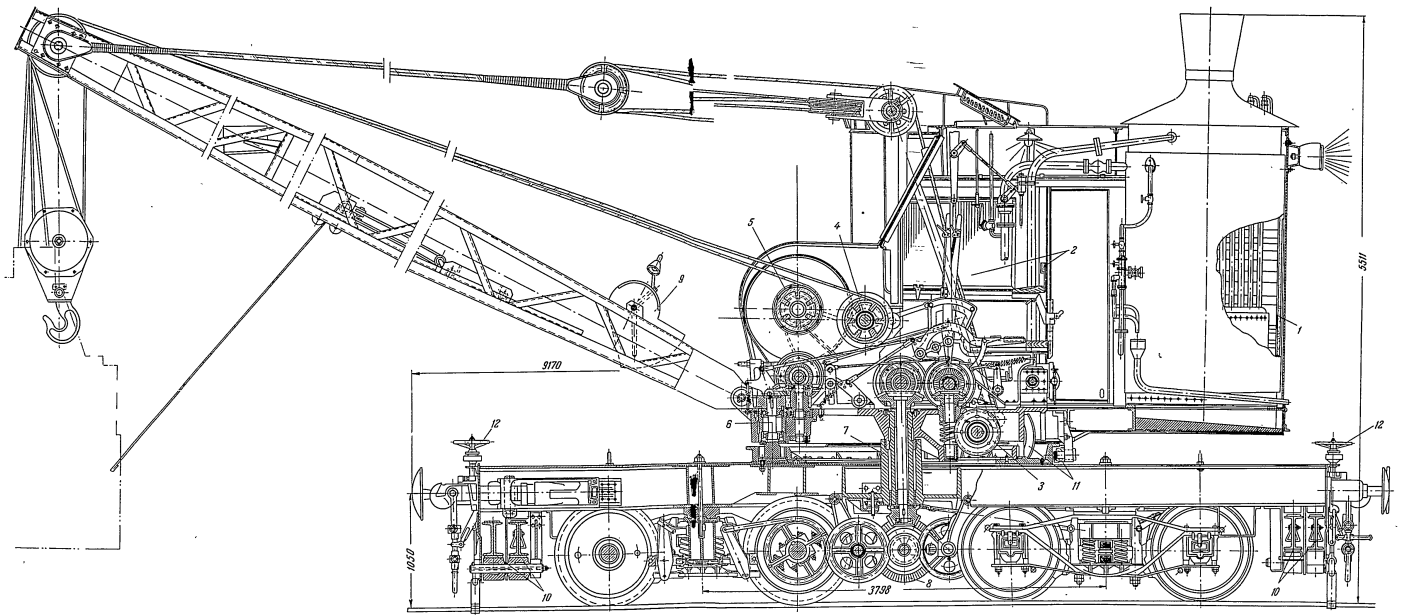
Продольный разрез и вид сбоку крана ПК-25.
